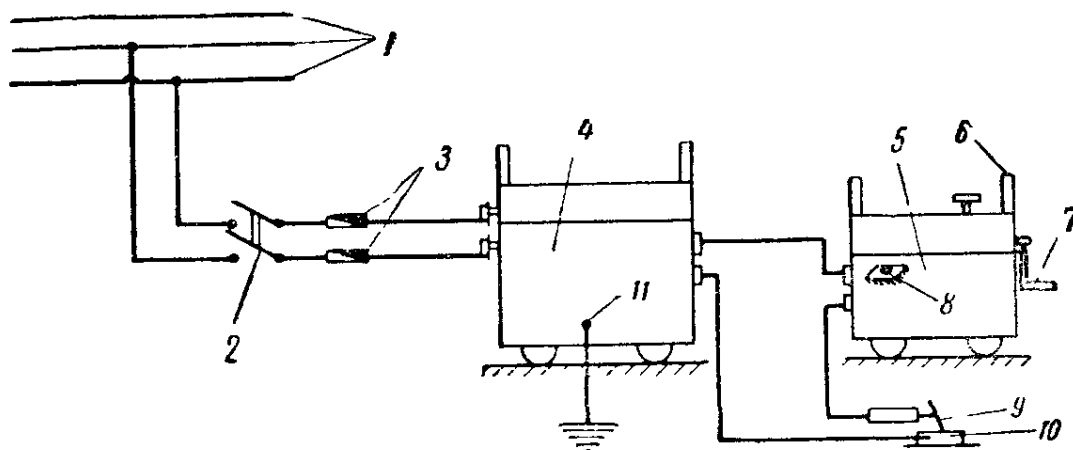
Схема соединения сварочного трансформатора и регулятора:
